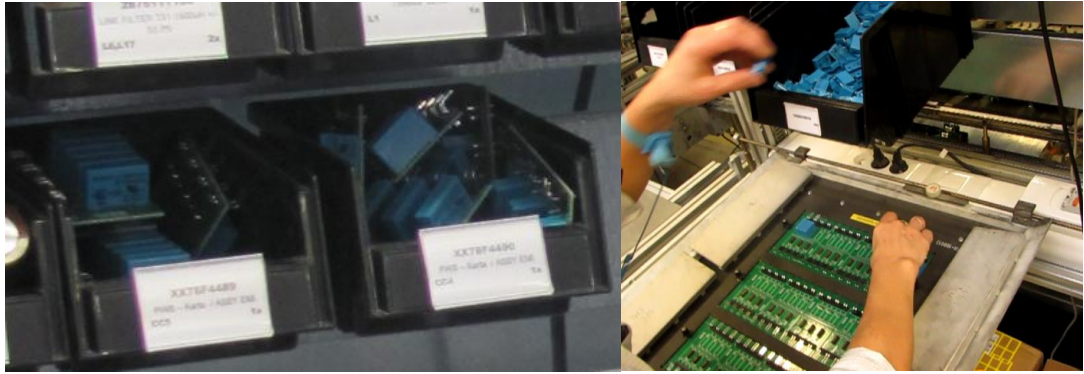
Pracovisko osádzania THT komponentov (Vlastné spracovanie)
